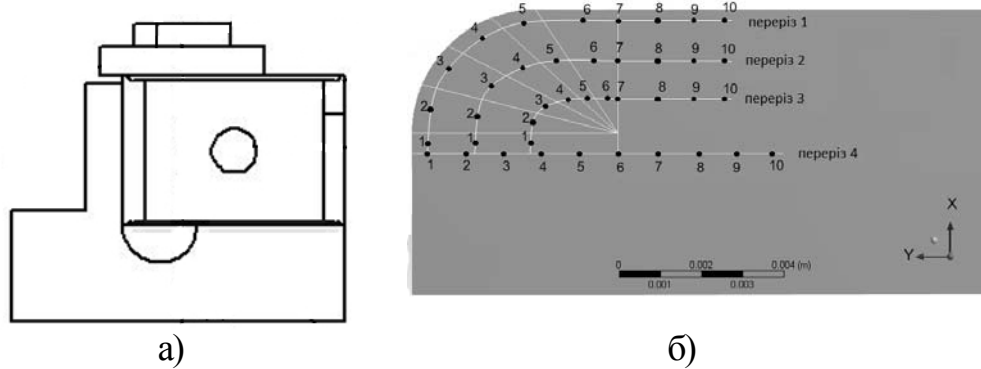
Базова конструкція збірного різця з призматичною пластинною (а) та розрахункова схема (б) для визначення напружено-деформованого стану різця
